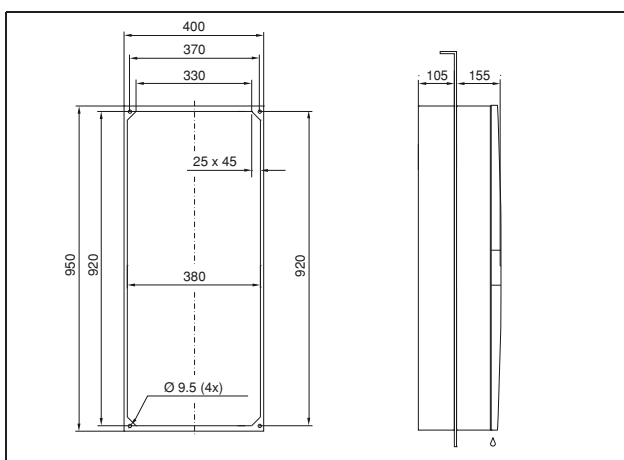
3304.xxx, 3305.xxx delinbyggnad
